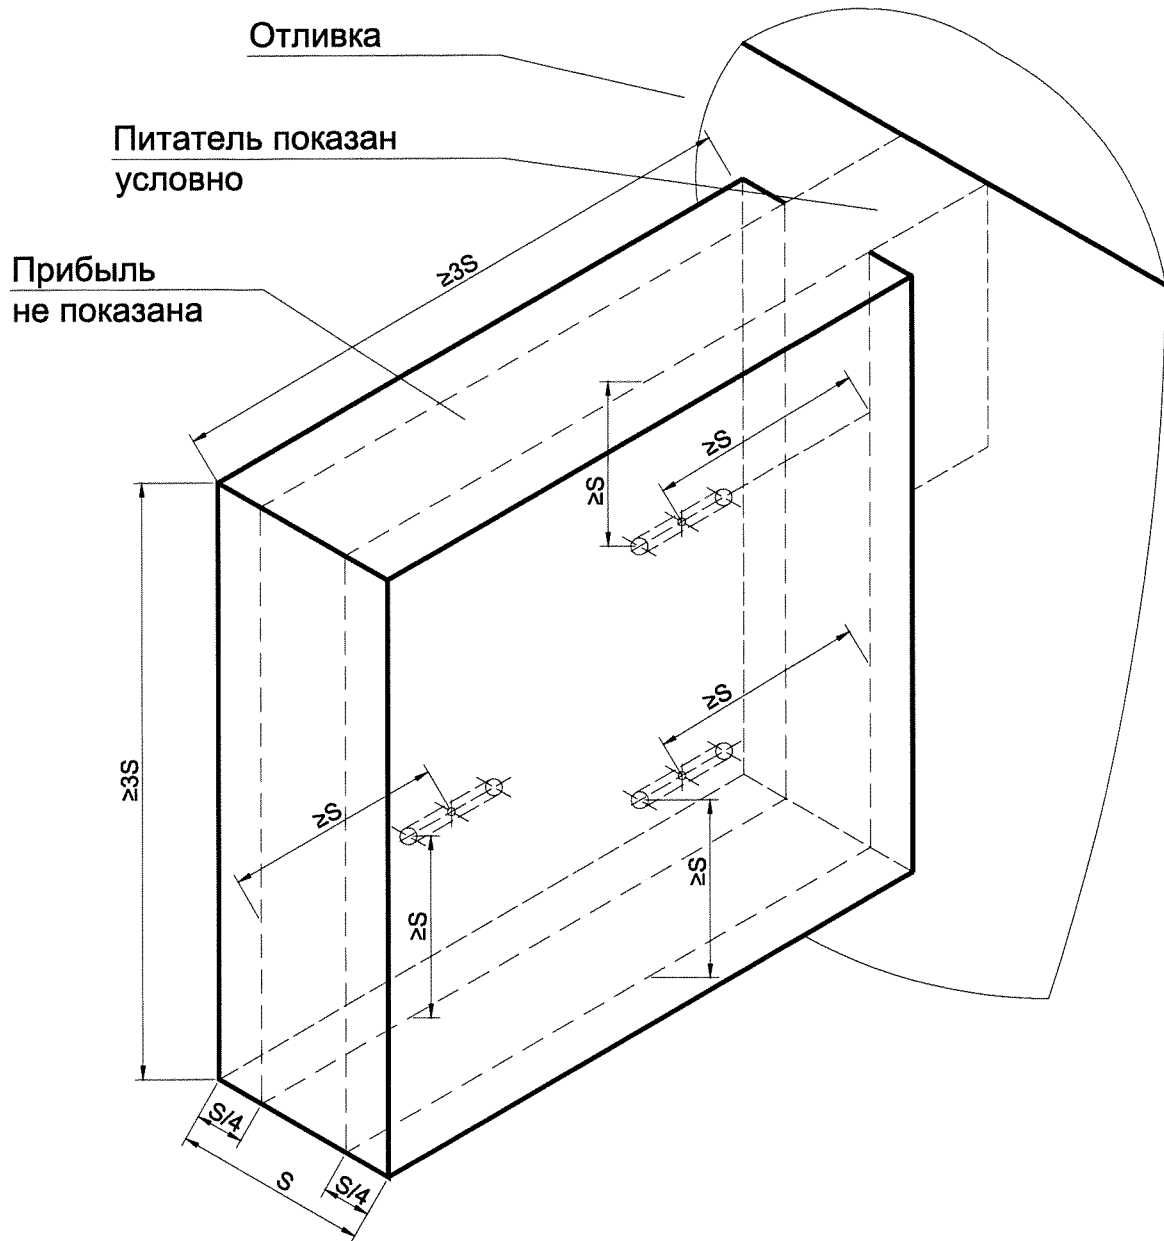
Схема отбора образцов для испытаний механических свойств из прилитой пробы
